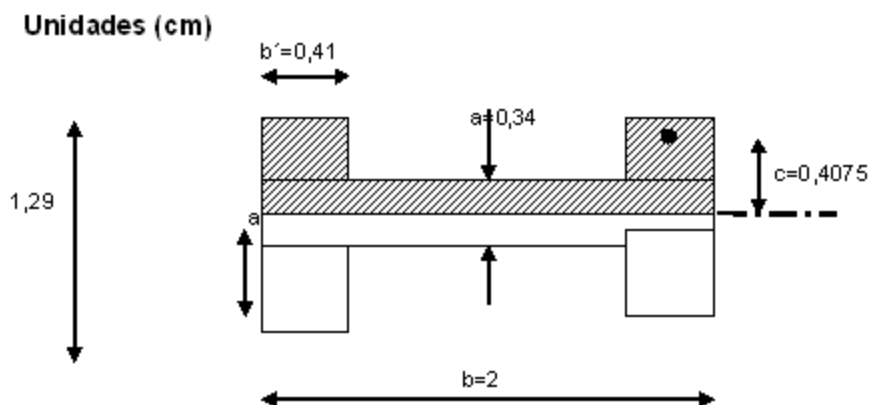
Sección Transversal Biela Volkswagen Gol
